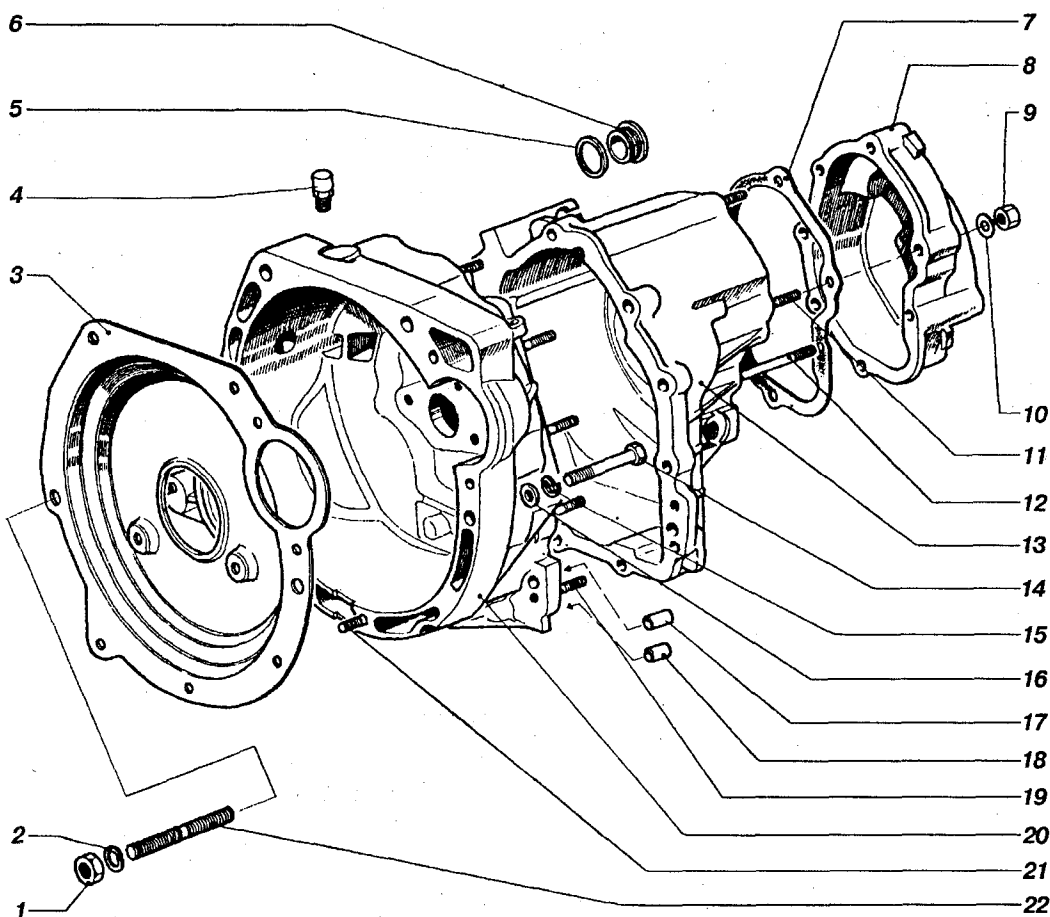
Картеры сцепления и коробки передач: 1 – гайка; 2 – шайба; 3 – защитный кожух; 4 – сапун в сборе; 5 – прокладка; 6 – пробка; 7 – прокладка задней крышки; 8 – задняя крышка; 9 – гайка; 10 – шайба; 11 – шпилька; 12 – шпилька; 13 – картер коробки передач; 14 – болт; 15 – шайба; 16 – шайба; 17 – штифт; 18 – штифт; 19 – шпилька; 20 – картер сцепления; 21 – шпилька; 22 – шпилька
